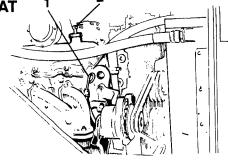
Moteur diesel 1 Jauge d'huile 2 Remplissage
